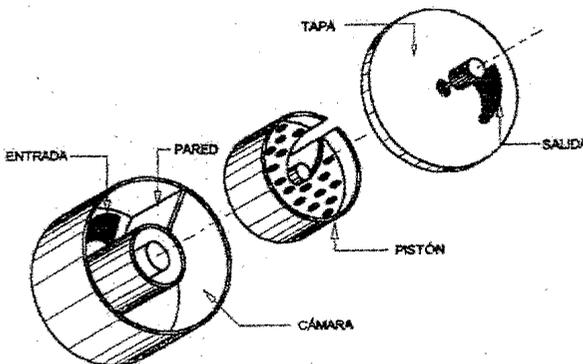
Elementos que componen el mecanismo del pistón oscilante.
